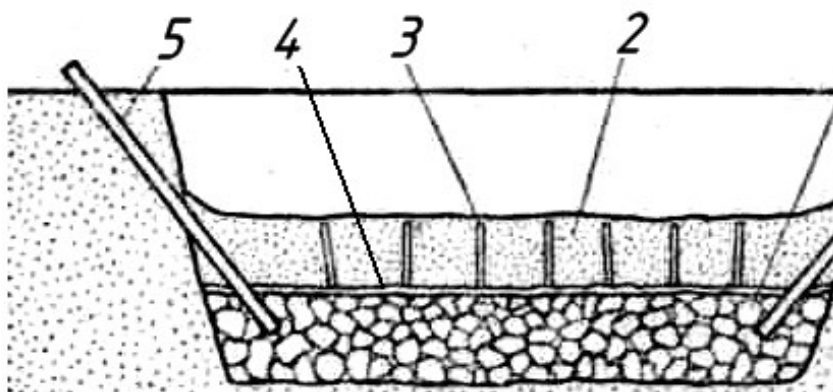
Твердая постель, подготовленная к формовке: 1 – слой кокса; 2 – формовочная смесь; 3 – вентиляционный канал; 4 – мешковина; 5 – труба
